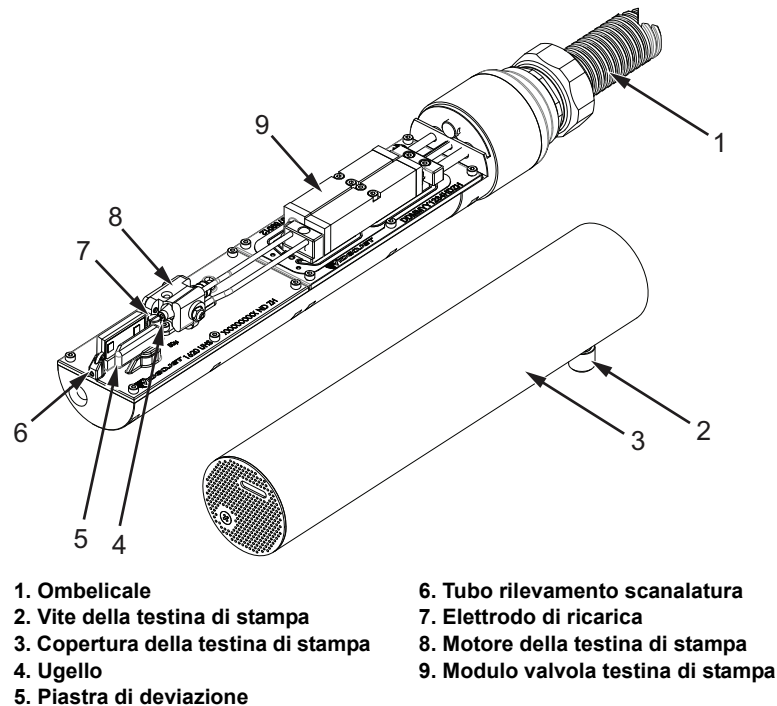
Testina di stampa (Videojet 1650 UHS)
